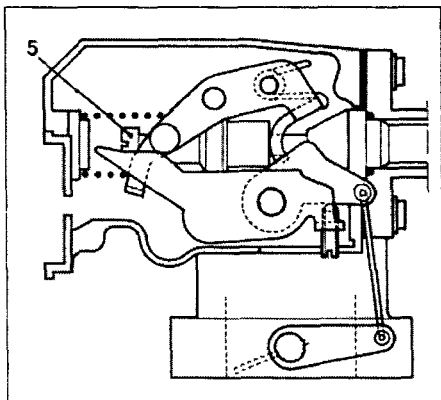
,б. 5 - винт регулировки зазора (а)
